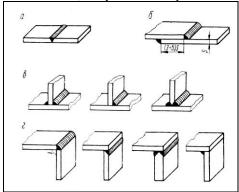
Виды сварных соединений: a) стыковое; б) нахлёсточное; в) тавровое; г) угловое
